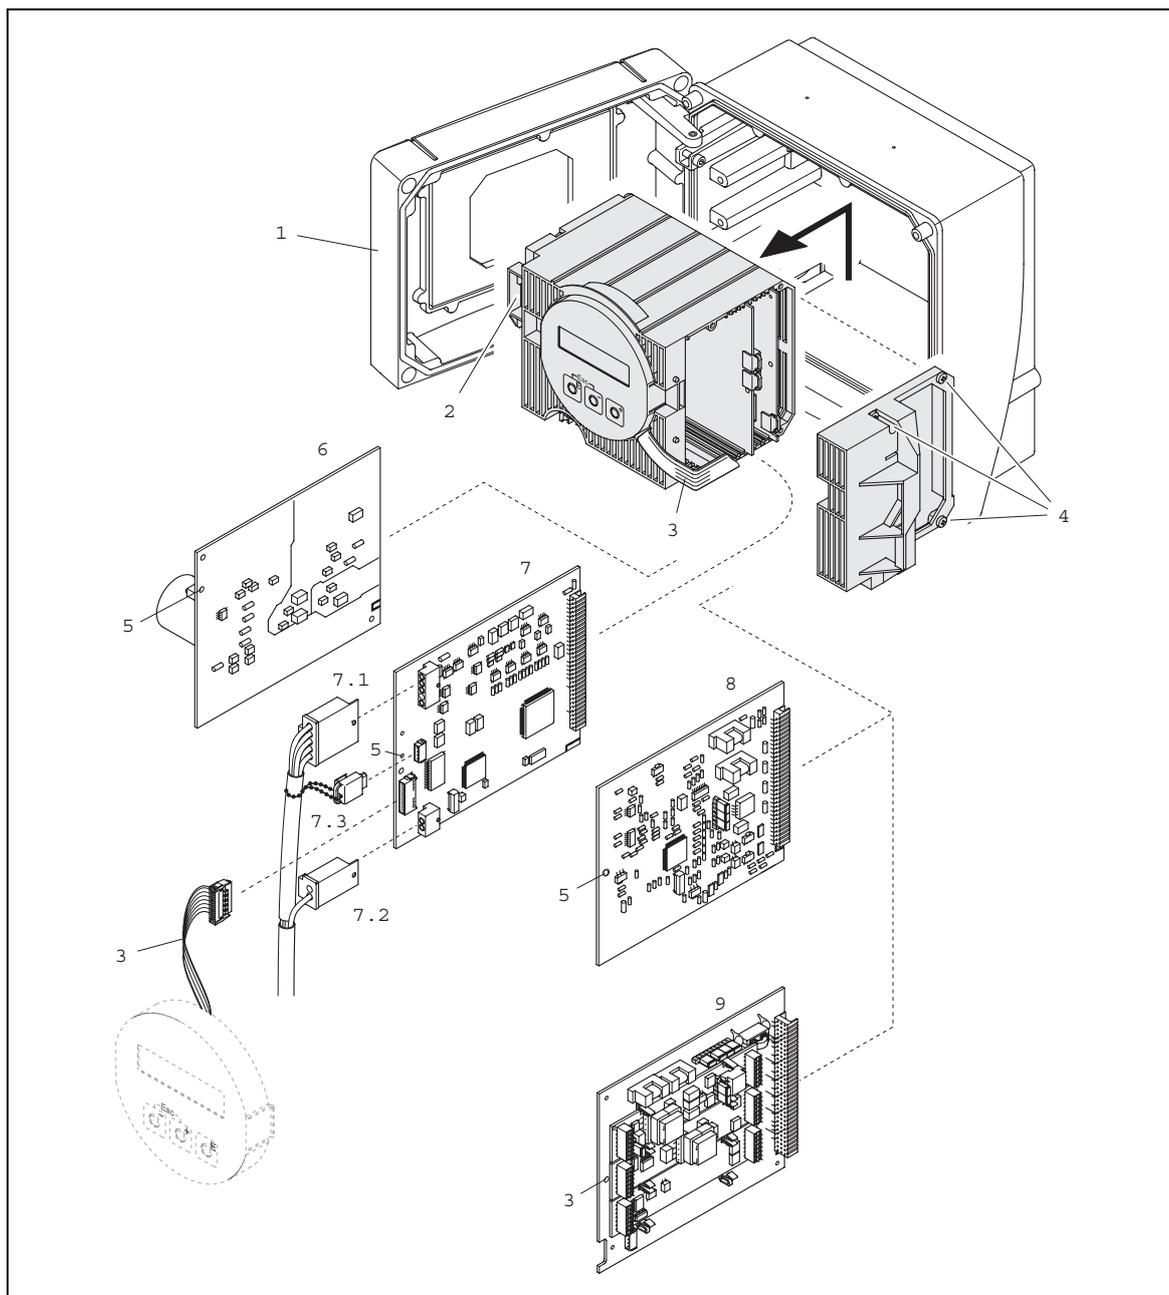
Корпус настенного исполнения: снятие и установка печатных плат
